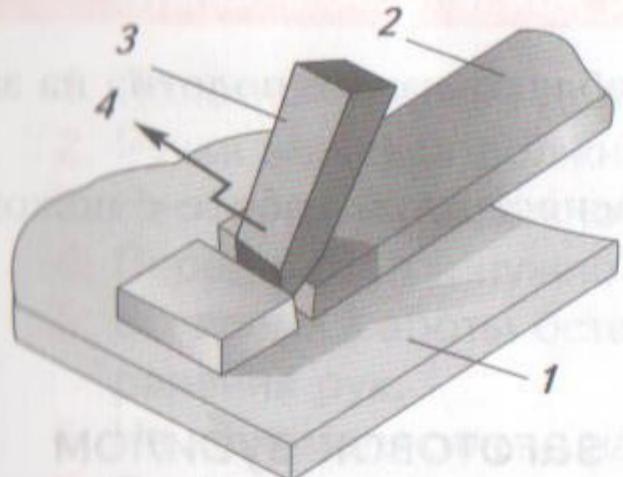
Рубка полосы на плите с наклоном зубила к линии разметки: 1 — плита; 2 — разрубаемая заготовка; 3 — зубило; 4 — направление перемещения зубила после каждого удара
